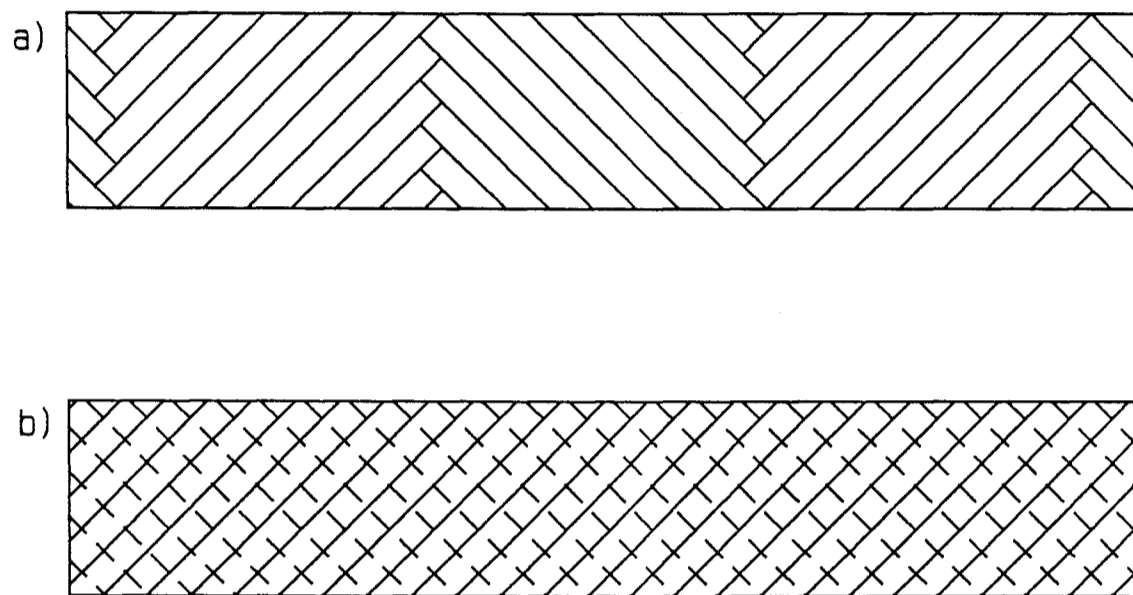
Sequência do posicionamento do reforço na fabricação pelo processo *filament winding*: a) bobinagem cruzada e b) bobinagem por superposição de camadas.
